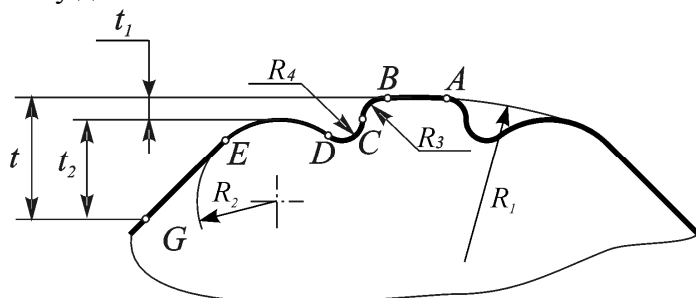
Режущая пластина с двумя ступенями для получистовой и чистовой обработки
